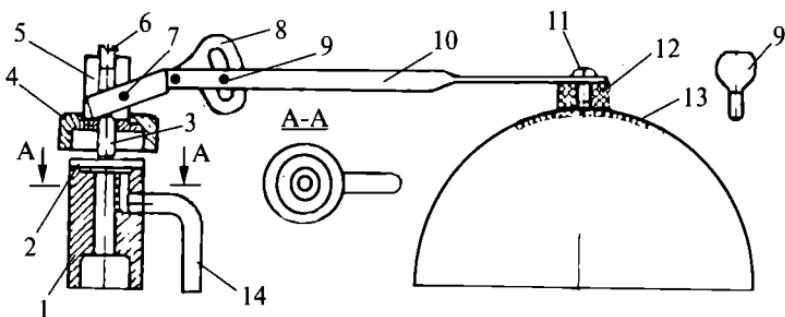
Вертикальный поплавковый клапан: 1 — корпус клапана; 2 — резиновая прокладка; 3 — шток; 4 — накидная гайка; 5 — валик; 6 — специальный винт; 7 — шплинты; 8 — рычаг фасонный; 9 — барашек; 10 — рычаг поплавка; 11 — винт; 12 — втулка пластмассовая; 13 — поплавок; 14 — трубка сливная
